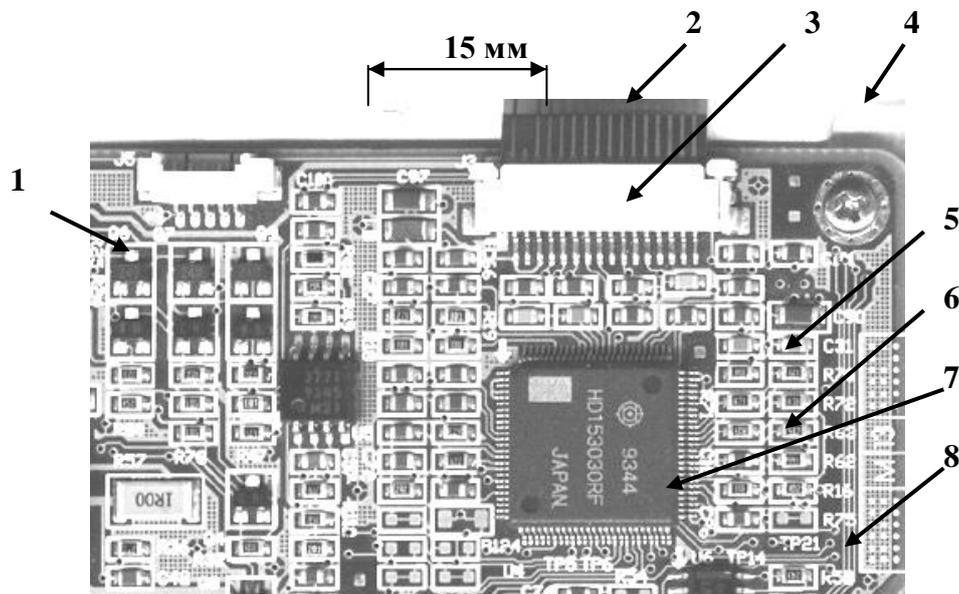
Конструкция бескорпусной тонкопленочной микросборки четвертого поколения [2]:
